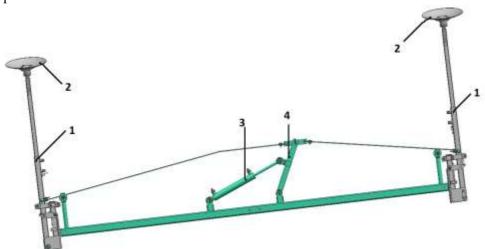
Маркеры гидрофицированные 1 — штанга; 2 — диски со ступицами ; 3 — гидроцилиндр; 4 — кронштейн для крепления тросиков
